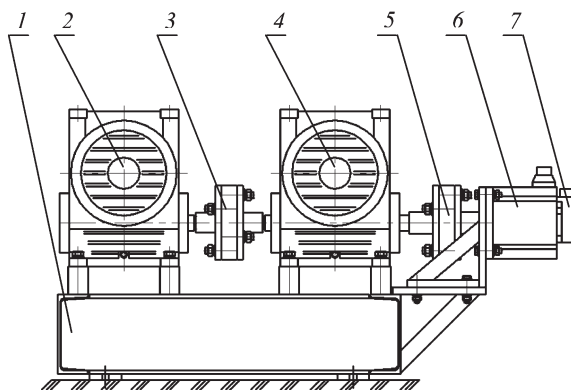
Общий вид привода тянущей клетки на базе серводвигателя: 1 – рама; 2, 4 – червячный редуктор привода тянущего вала; 3, 5 – пальцевая муфта с упругим диском; 6 – серводвигатель; 7 – встроенный в двигатель импульсный датчик
